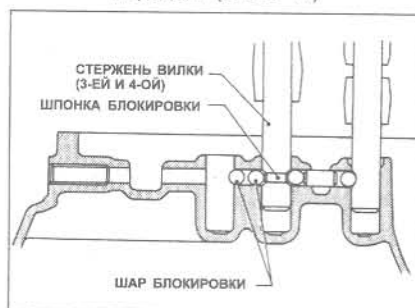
Шары блокировки в стержне вилки смещения 3/4 передач (Глава 14)
